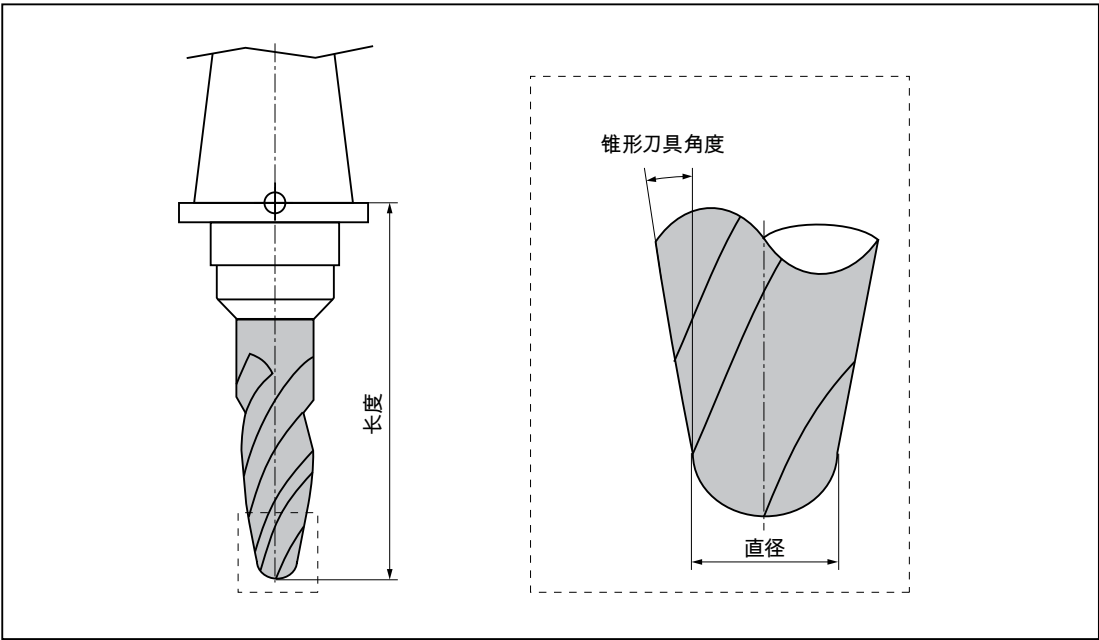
3D 刀具，例如：圆锥形锻模铣刀（157 型）
